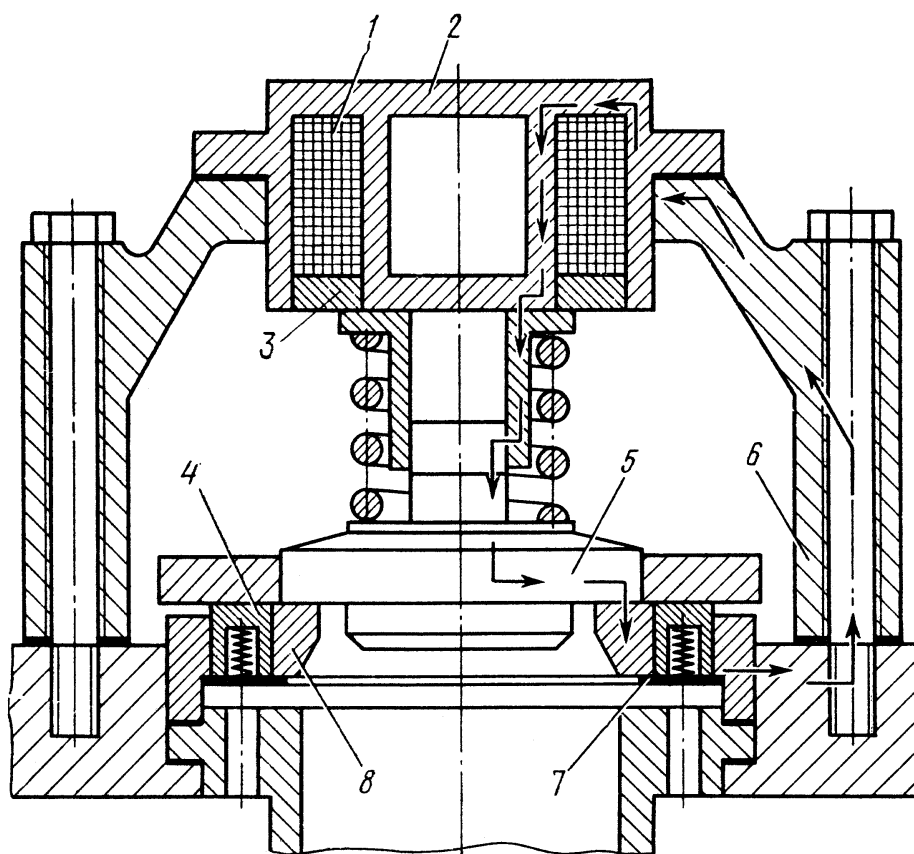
Схема электромагнитного отжима пластины всасывающего клапана: 1 – катушка электромагнита; 2 – корпус электромагнита; 3, 4 – немагнитные вставки; 5 – нагнетательный клапан; 6 – проставка компрессора; 7 – пластина всасывающего клапана; 8 – корпус всасывающего клапана
